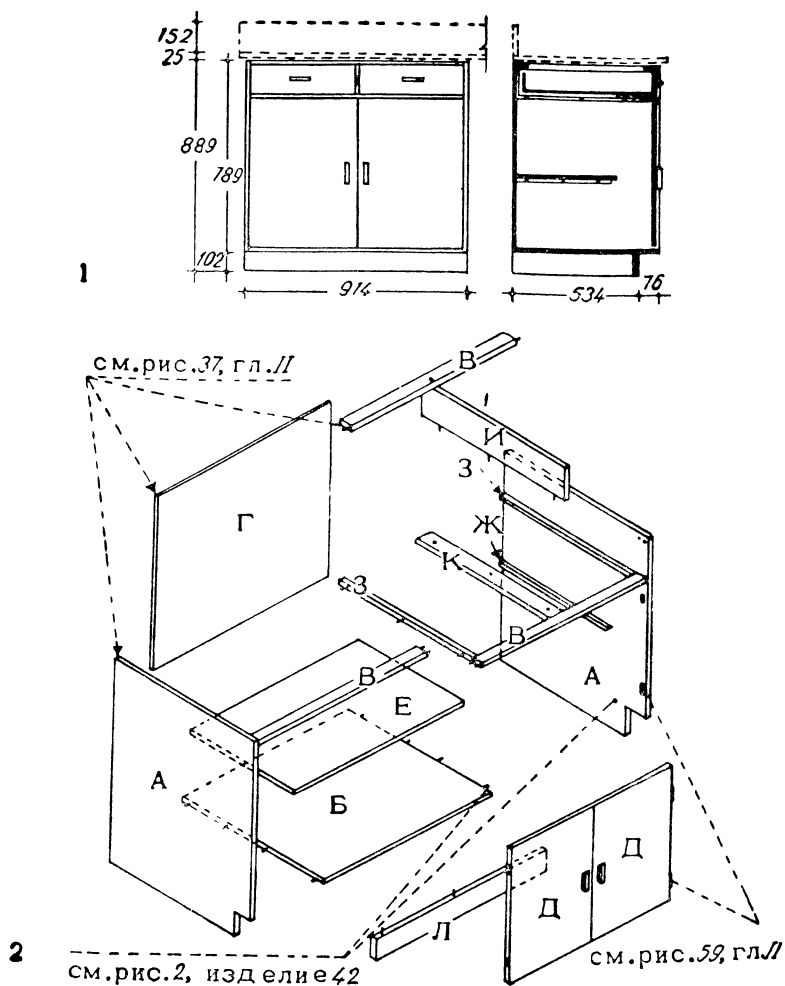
2. 1 — вид спереди и разрез, 2 — эскиз сборки деталей.
